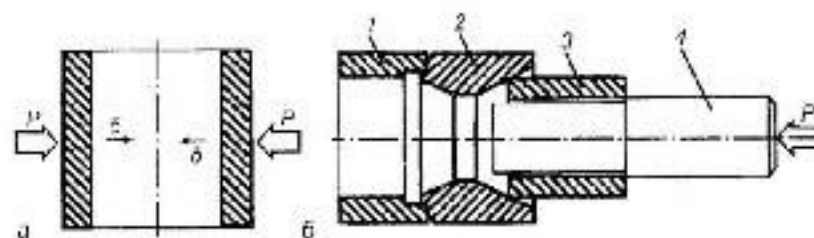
Схема пластического деформирования обжатием: а — принципиальная схема; б — схема приспособления для обжатия втулок; 1 — опорное кольцо; 2 — матрица; 3 — восстанавливаемая втулка; 4 — оправка
